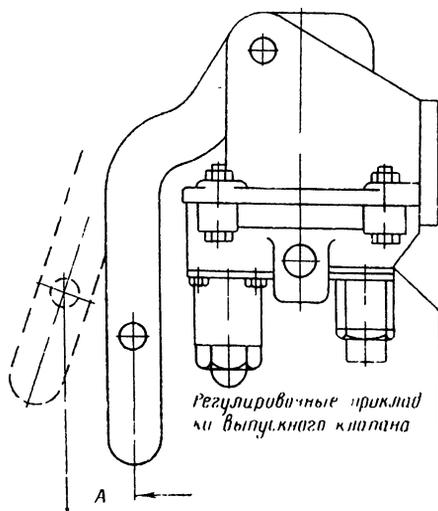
Регулировка хода выпускного клапана после сборки тормозного крана
